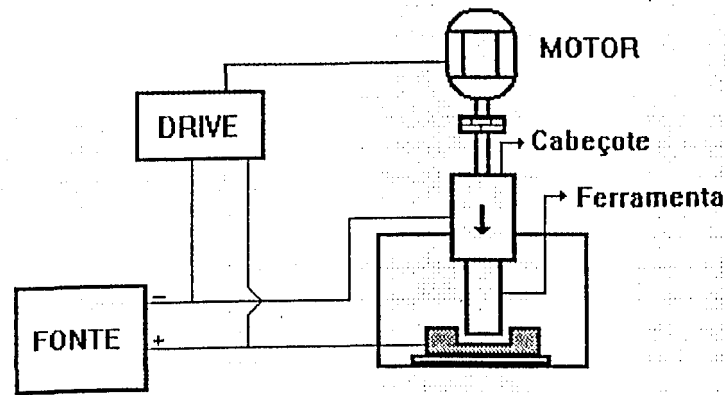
Esquema simplificado do mecanismo de avanço da ferramenta de um equipamento de usinagem eletroquímica.
